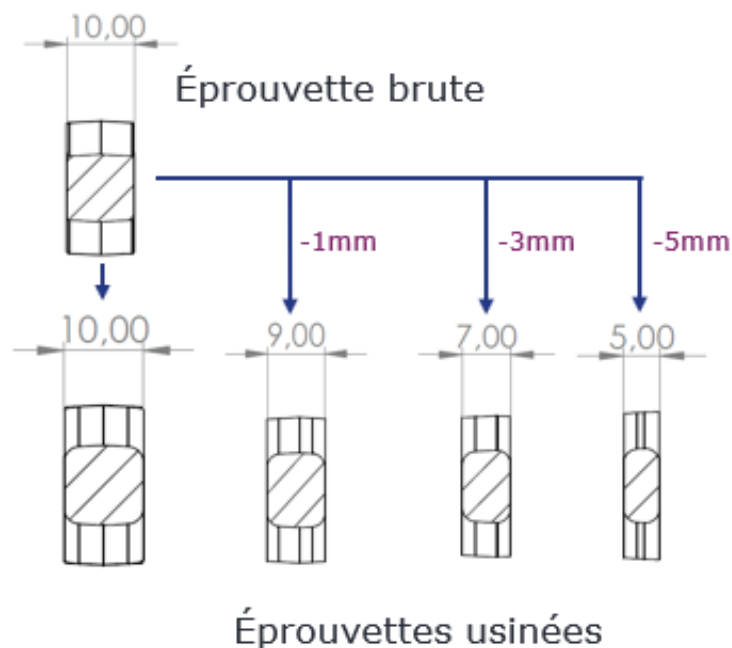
Schéma de la réduction d'épaisseur de l'éprouvette brute pour la fabrication des éprouvettes de fatigue, faces usinées côtés droits et faces brutes côtés gauches
